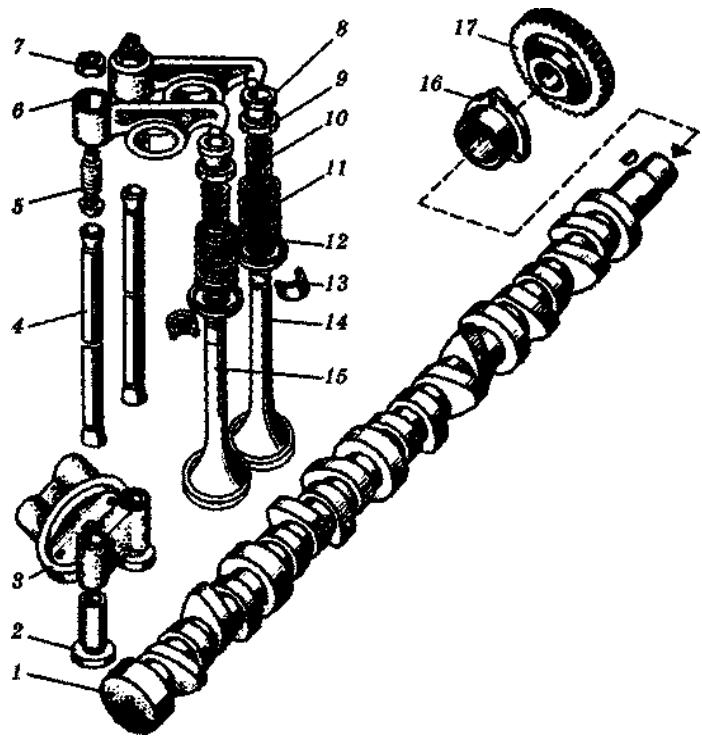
Схема газорозподільного механізму дизеля КамАЗ-740:
